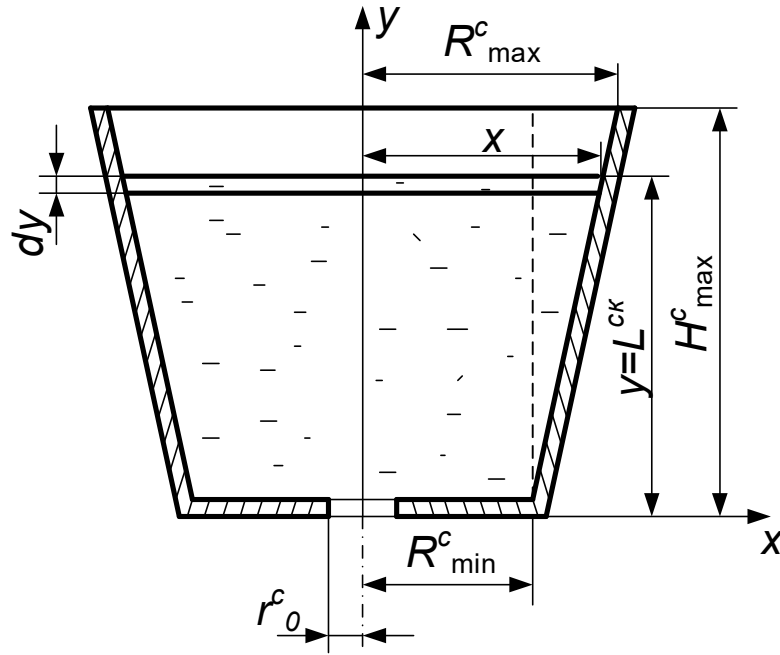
Расчетная схема сталеразливочного ковша
